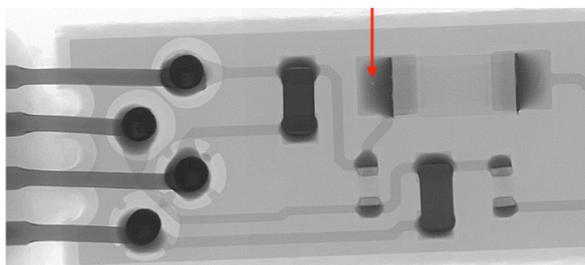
Radiografía digital de los componentes electrónicos de la tablilla del sensor, vista a mayores aumentos, la flecha roja indica un poro en el interior de la soldadura aplicada.
